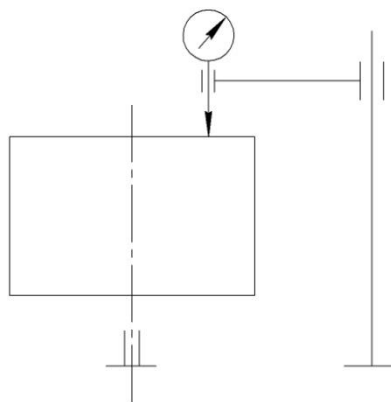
Ескіз схеми контролю торцевого биття
